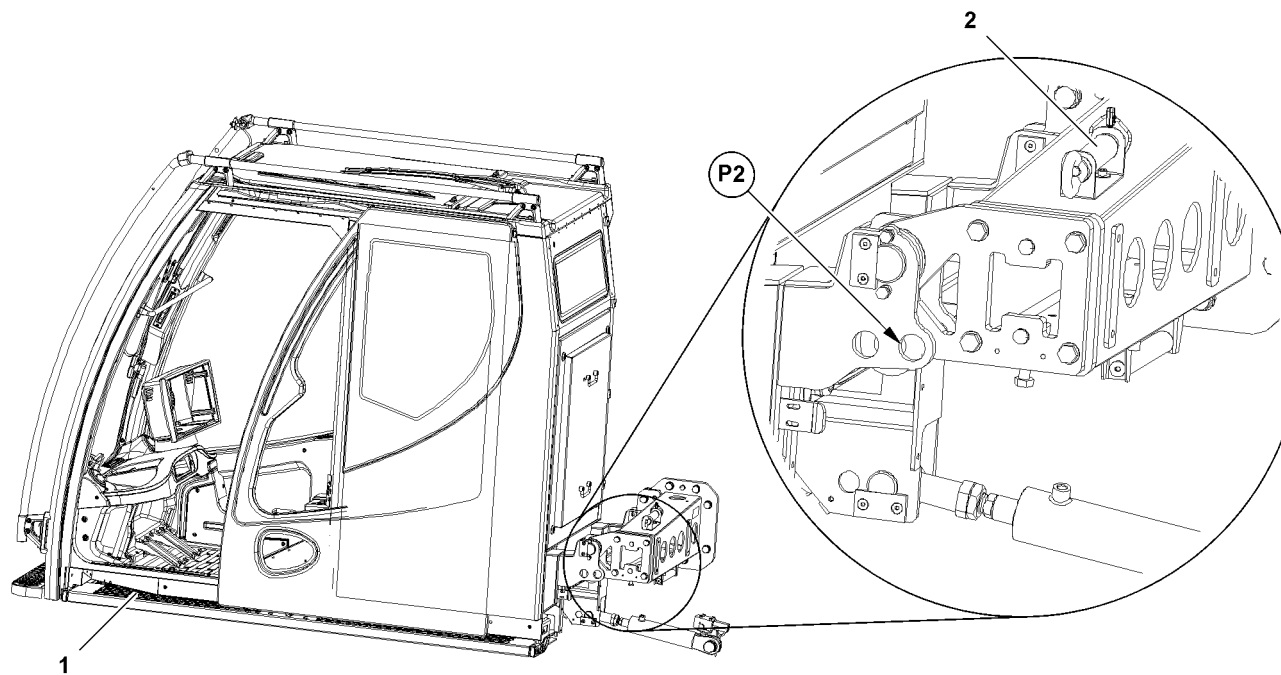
Cabine do motorista do guindaste, posição horizontal
